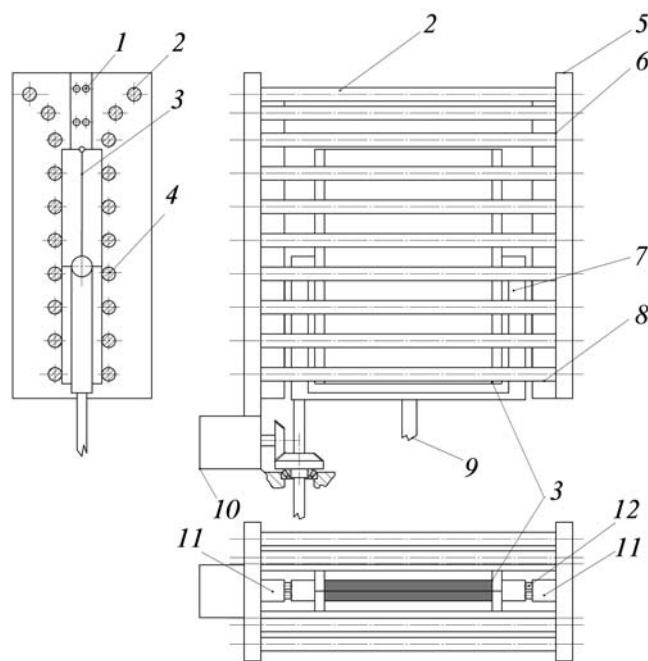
Модуль рамочного держателя подложек с раскрывающейся подложконесущей поверхностью (насадка-рама в сборе с державкой):
